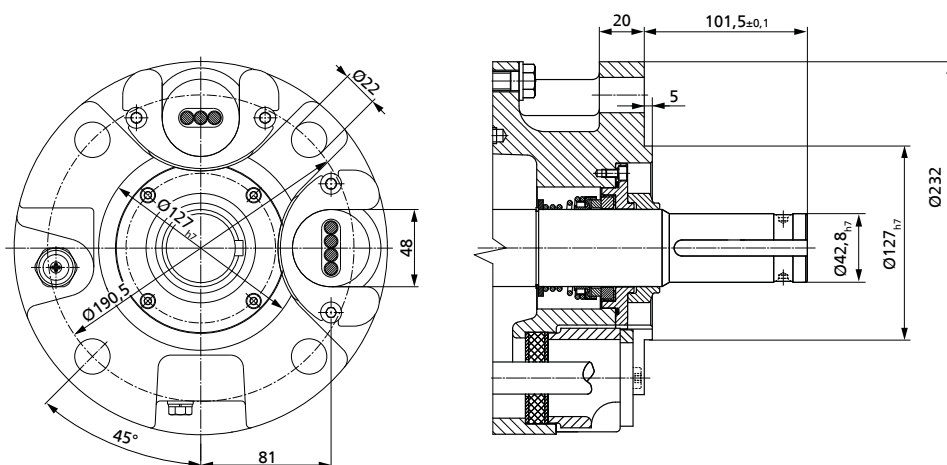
Присоединительный размер UMA 250D, данные размера [мм]
